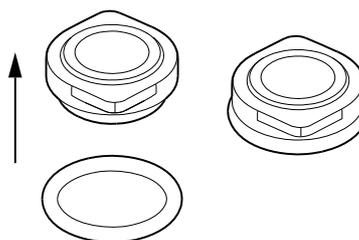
Монтаж уплотнительного кольца на неподвижной части торцевого уплотнения
